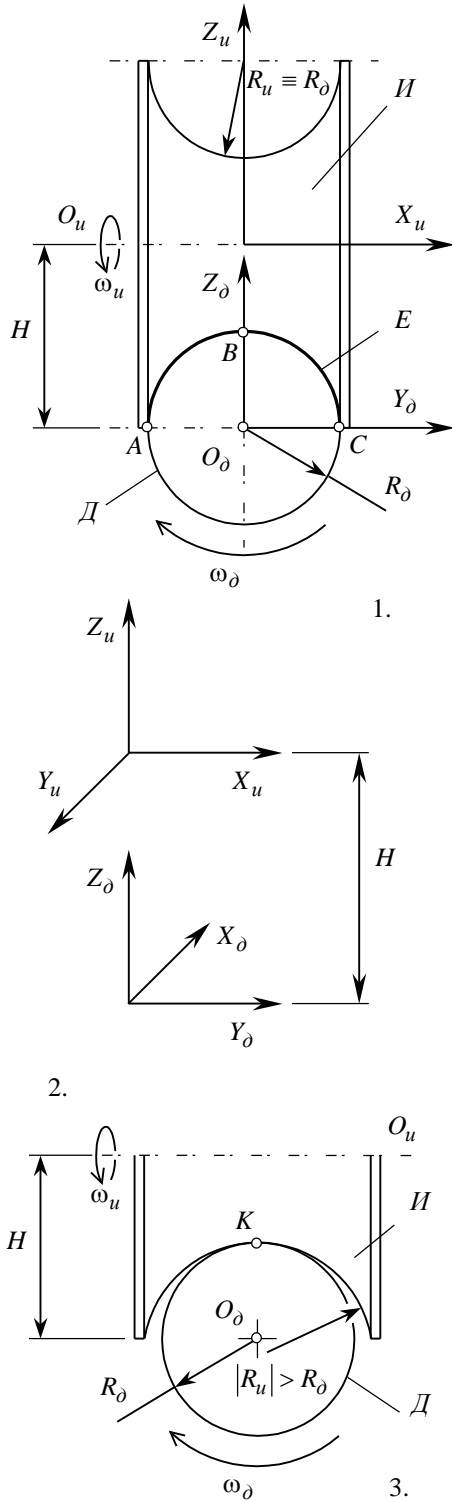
Образование исходной инструментальной поверхности при однопараметрической кинематической схеме формообразования.
